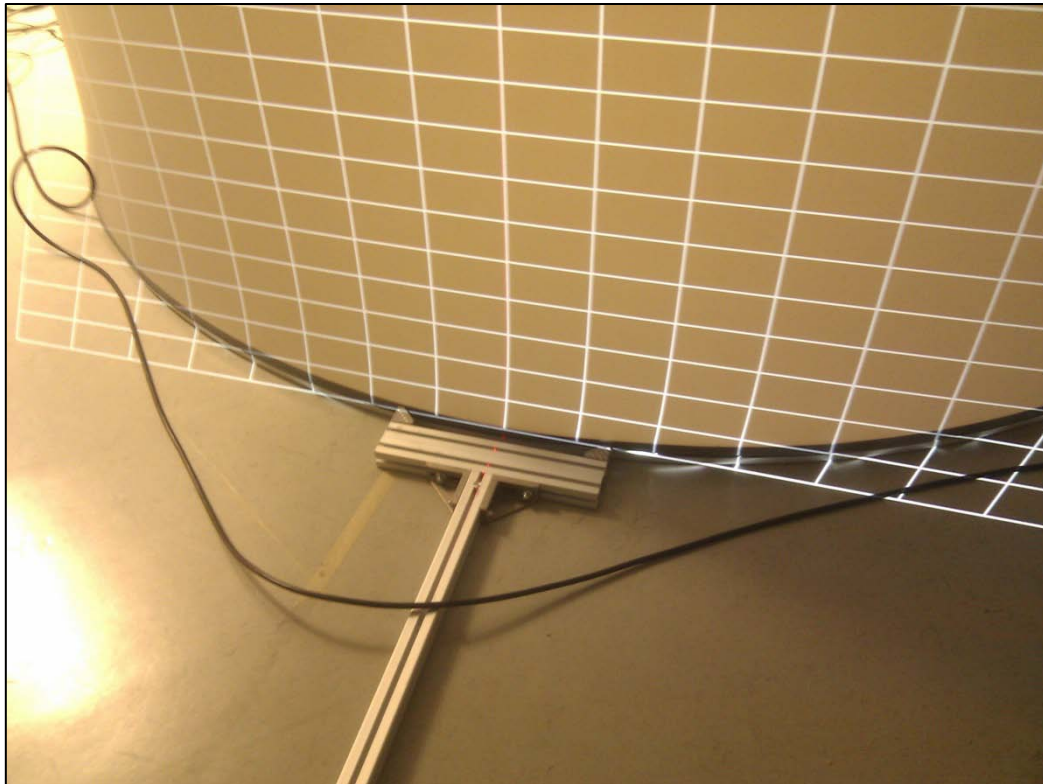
Werkzeug wird mit Hilfe der Laserwasserwaage am Radius ausgerichtet.
